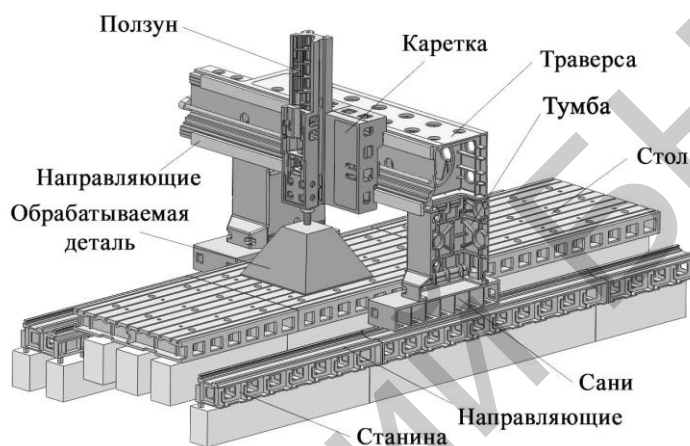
Трехмерная геометрическая модель несущей системы продольно-фрезерного станка с подвижным порталом
